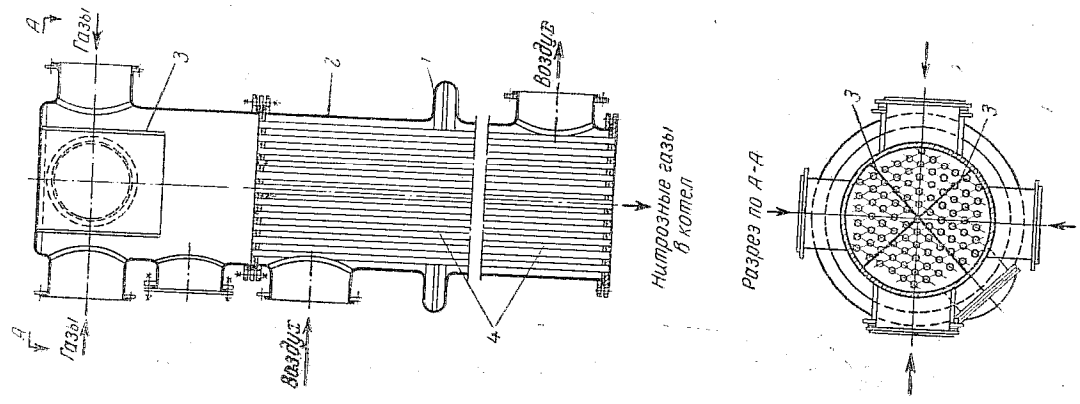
Подогреватель воздуха (поверхность нагрева 50 м^2): 1—компенсатор; 2—корпус; 3—перегородки; 4—трубки.
